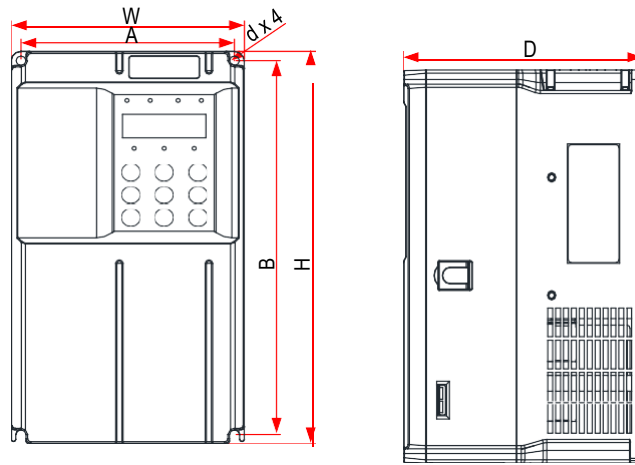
GT600-4T0.4GB ~ GT600-4T15GB 外型尺寸及安装尺寸示意图
